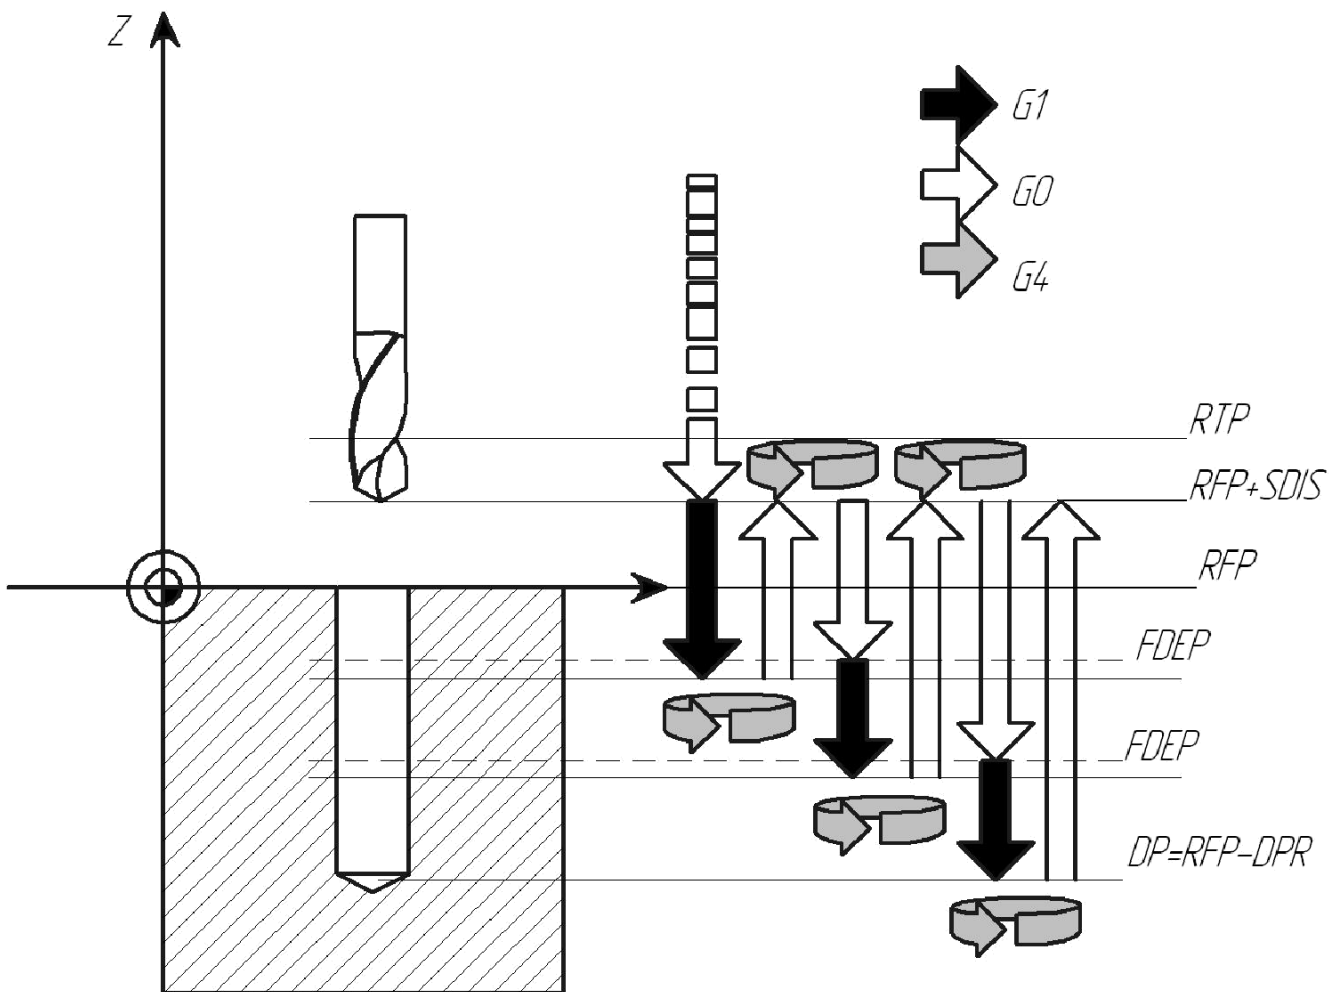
Глубокое сверление с удалением стружки (VARI=1)
